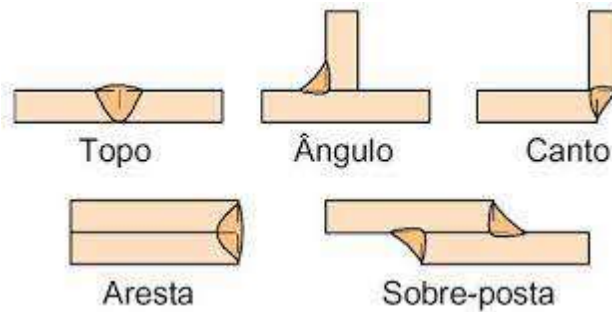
Alguns tipos de junta para soldagem com eletrodo revestido.
